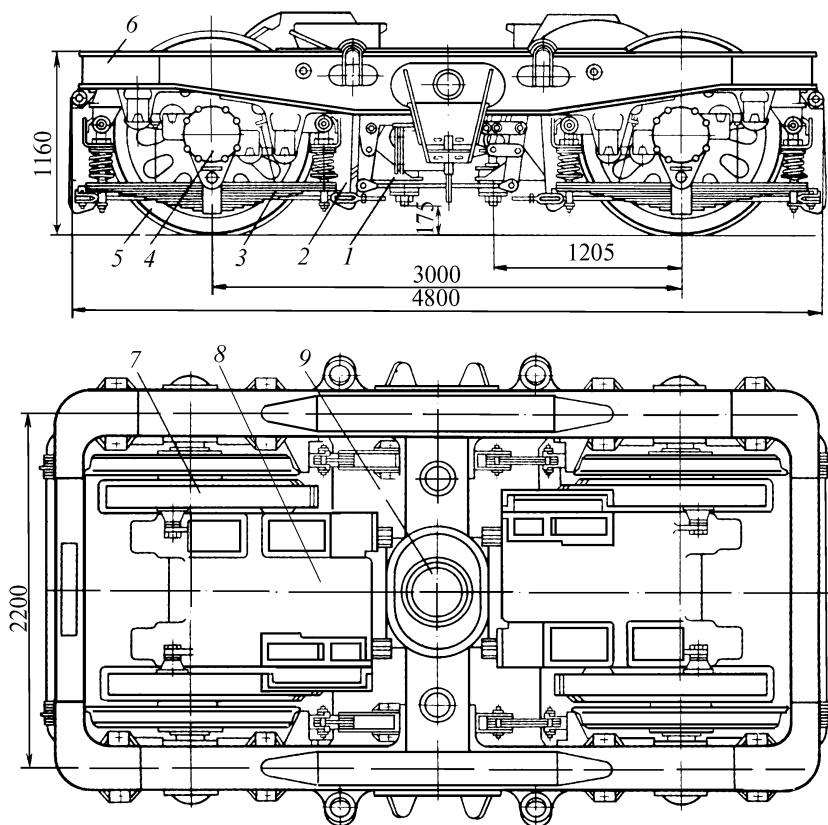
Тележка электровоза ВЛ80с: 1 — элементы подвешивания тягового двигателя; 2 — элементы тормозной рычажной передачи; 3 — элементы рессорного подвешивания буксового узла (листовая рессора и две рессорные стойки с пружинами); 4 — буксовый узел (роликовая букса и два поводка); 5 — колесная пара; 6 — рама тележки; 7 — кожух зубчатой передачи; 8 — тяговый двигатель; 9 — узел связи со шкворнем (шаровая связь шкворня)
